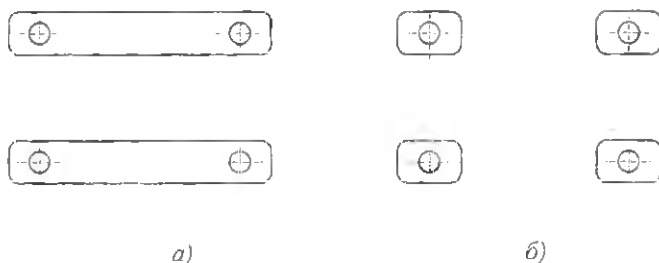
Варианты опорных поверхностей корпуса редуктора
